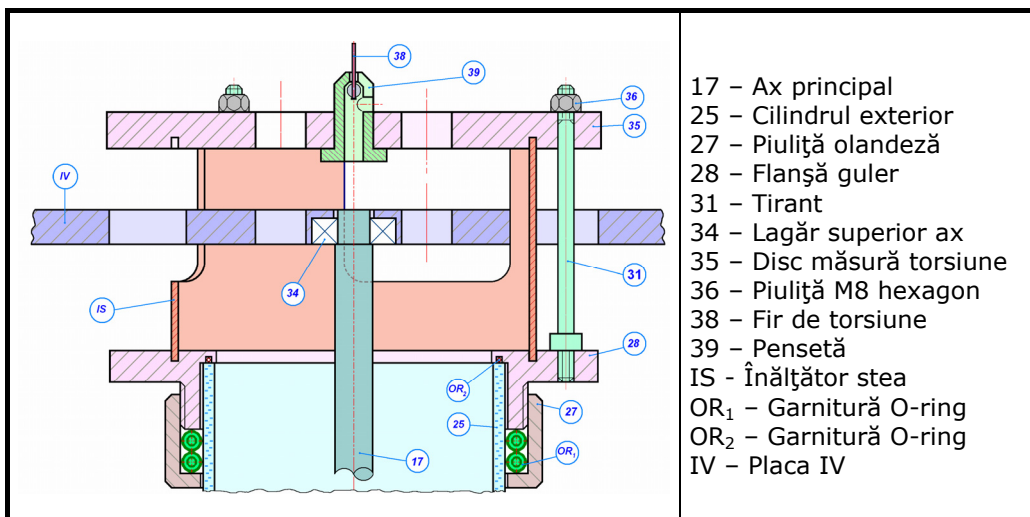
Montajul cu tiranți și înălțător stea a discului de măsură pe flanșa cilindrului exterior
